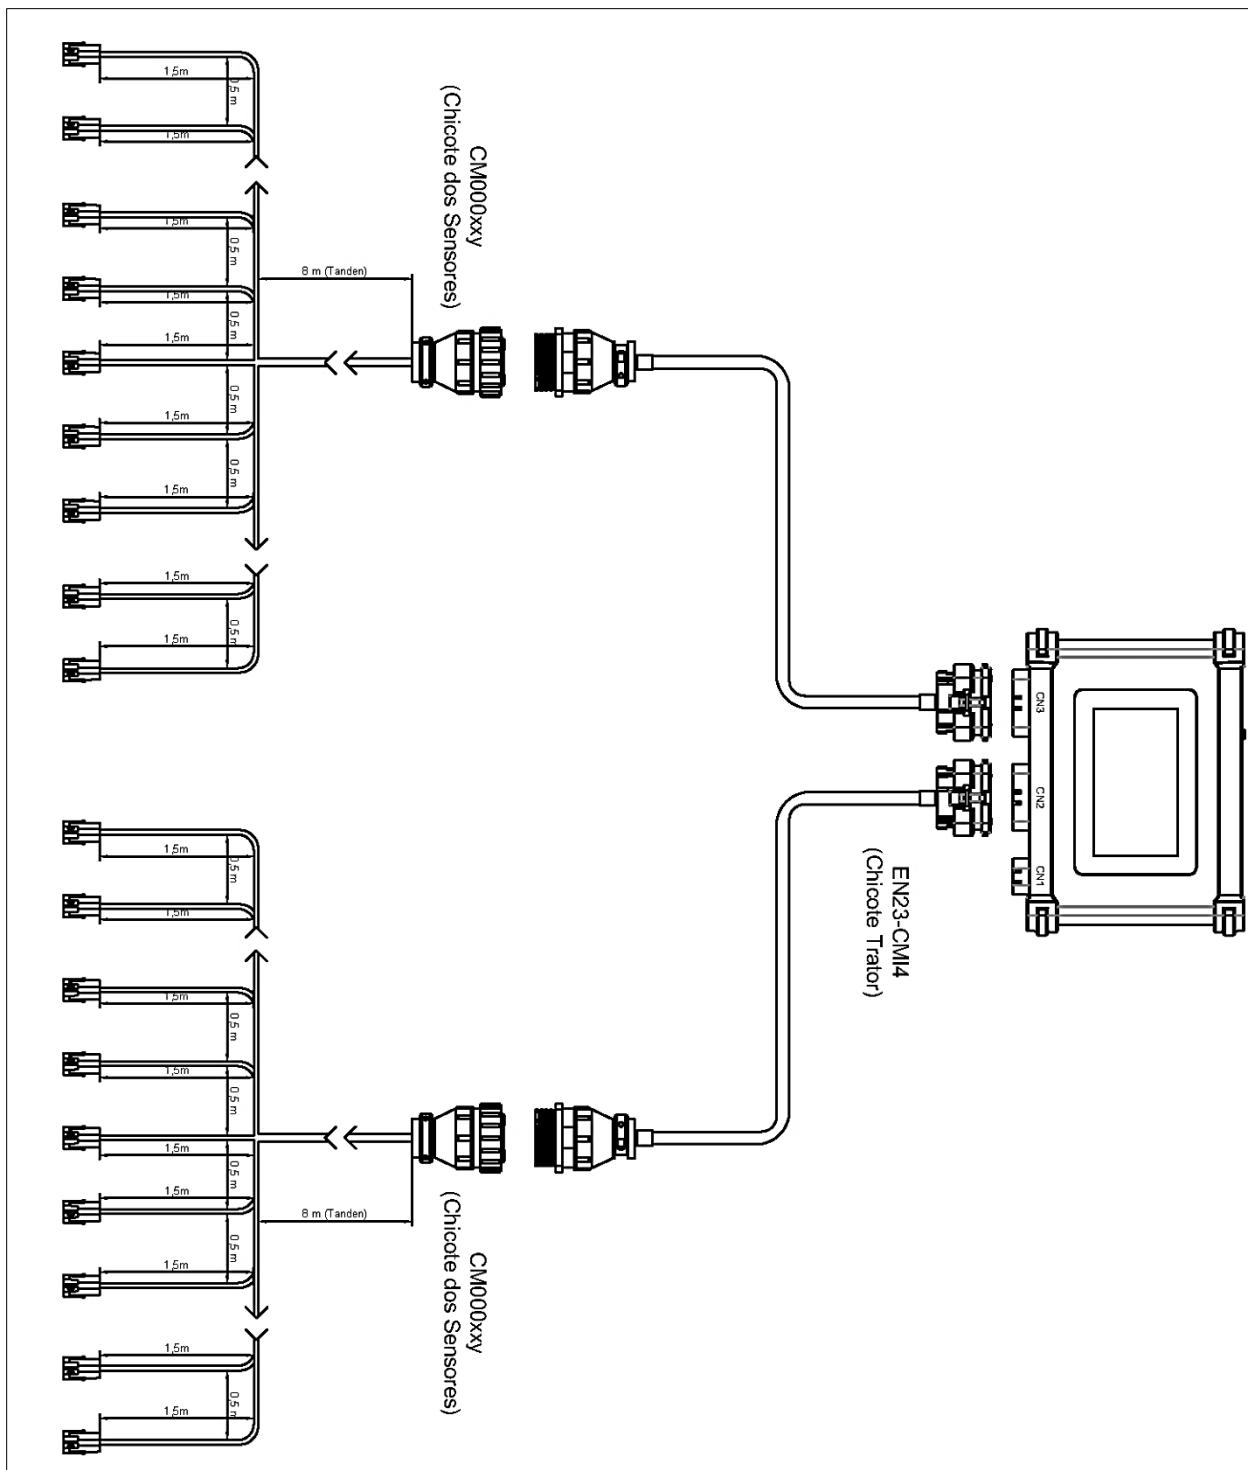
Esquema de montaje para implemento de plantación en configuración tandem
